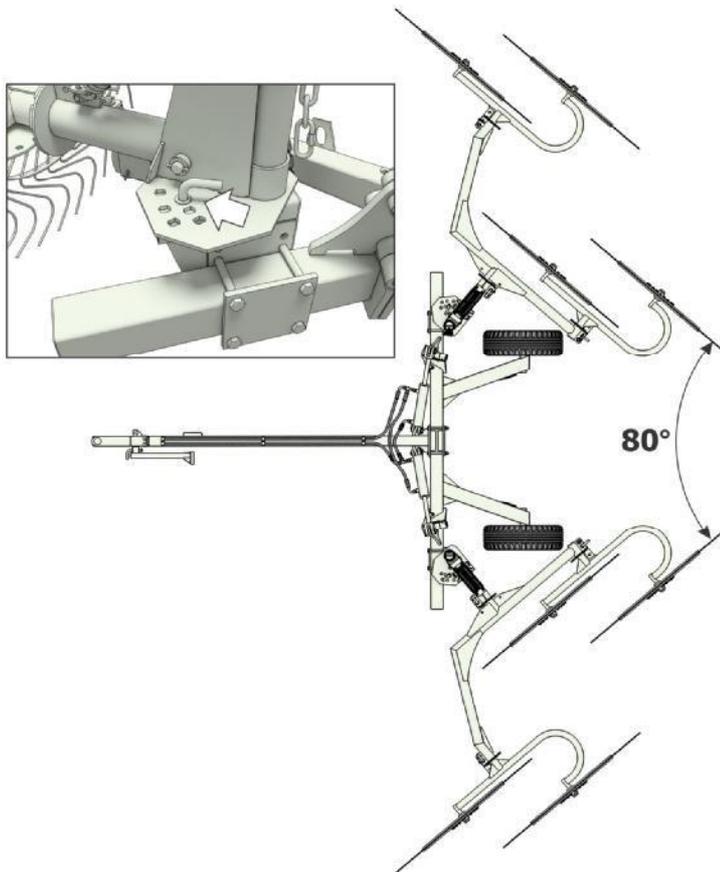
Схема установки секций рабочих колес при оборачивании валка
